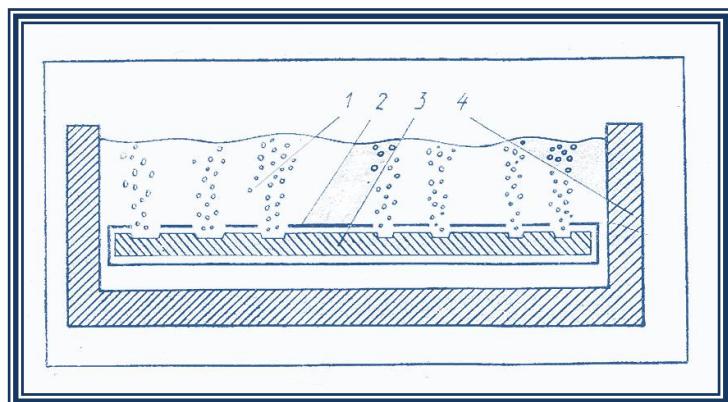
Схема процесу хімічного травлення: травильний розчин; 2 – шар захисного лаку; 3 – виріб; 4 – корпус ванни
